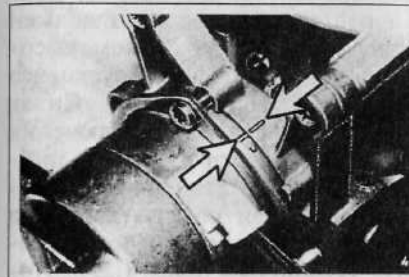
Регулировка автоматического пускового устройства. Указанные стрелками маркировочные риски должны совпадать.
